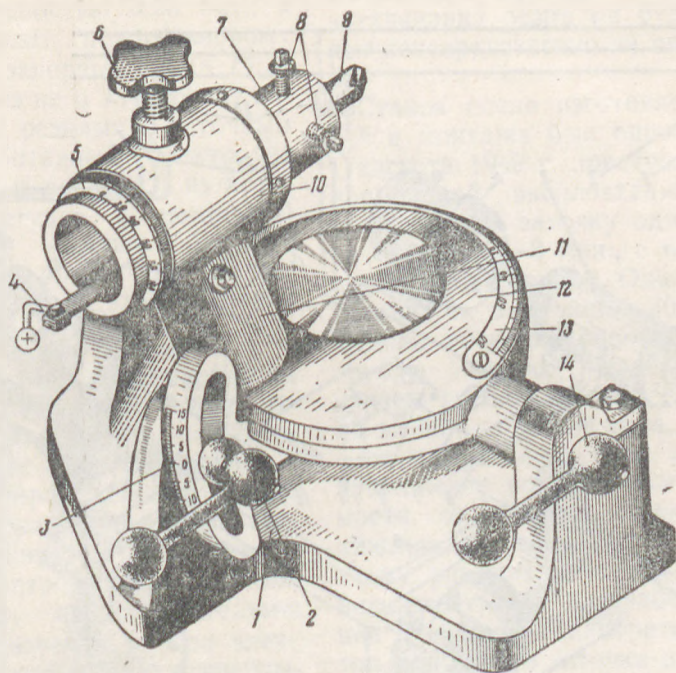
Головка-резцедержатель станка анодно-механической заточки
